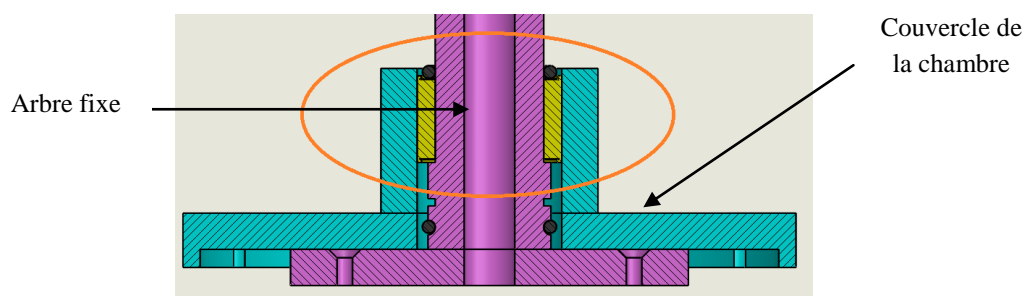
Assemblage de l'arbre fixe avec le couvercle de la chambre.
